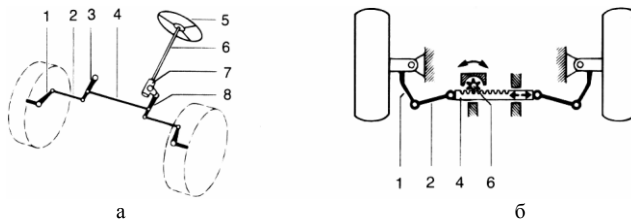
Схема рулевого управления: *а* – с шариковой гайкой; *б* – реечное рулевое управление; 1 – рычаг поворотного кулака; 2 – боковая рулевая тяга; 3 – маятниковый рычаг; 4 – поперечная рулевая тяга или зубчатая рейка; 5 – рулевое колесо; 6 – рулевой вал; 7 – картер рулевого механизма; 8 – рулевая сошка.
